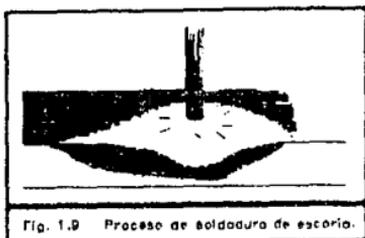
Proceso de soldadura de escoria.
